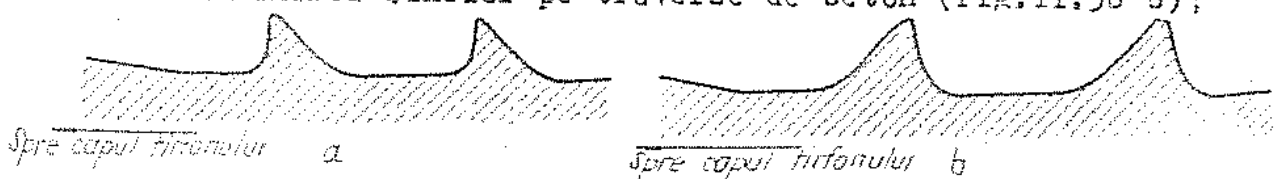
Filetul tirfoanelor; a/ pentru traverse de lemn; b/ pentru traverse de beton
